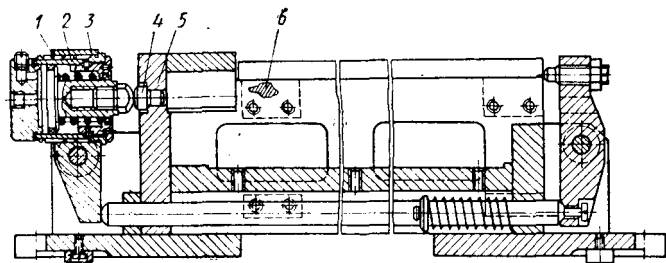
Универсально-наладочное фрезерное приспособление с гидроприводом
